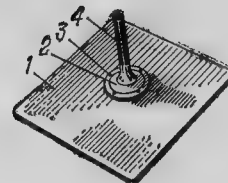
1 — полотно; 2 — фланец; 3 — прокладка; 4 — ручка
